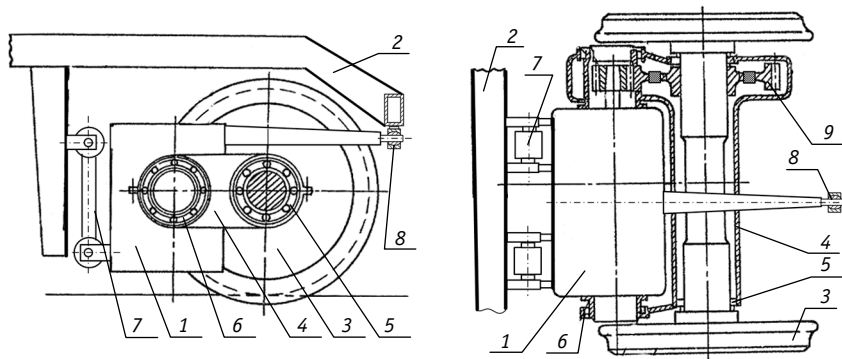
Схема опорно-рамного привода без передаточного механизма:
